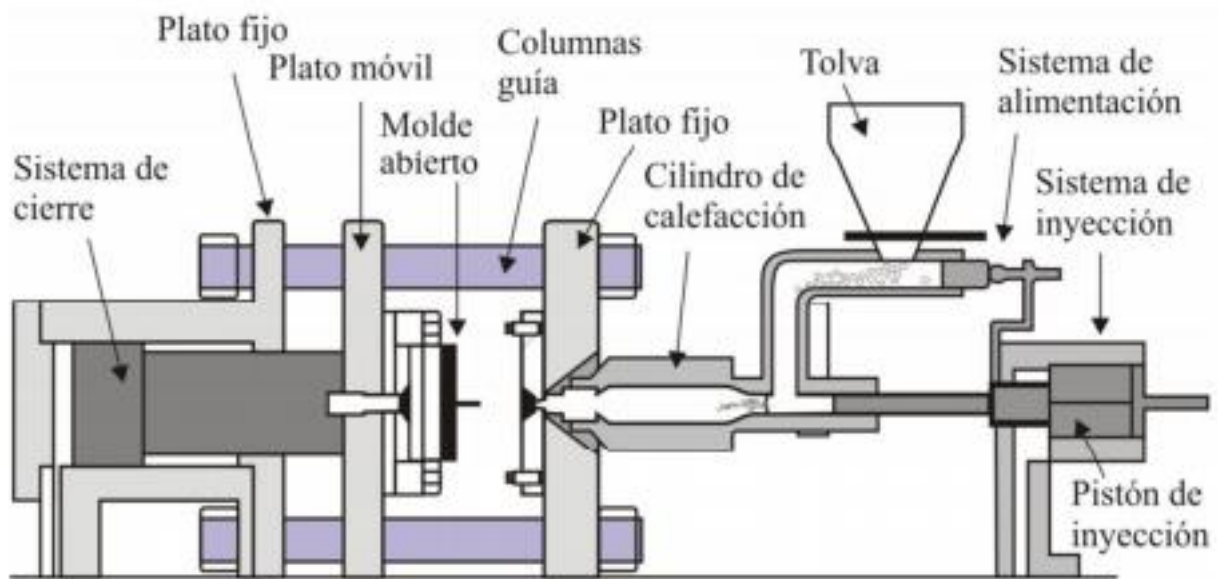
Esquema de una máquina de moldeo por inyección con pistón
